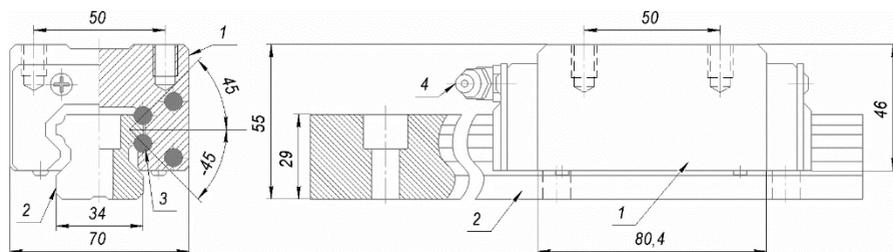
Рельсовая направляющая качения с каретками HSR35R: 1 – каретка; 2 – рельс; 3 – шарики; 4 – смазочный ниппель
